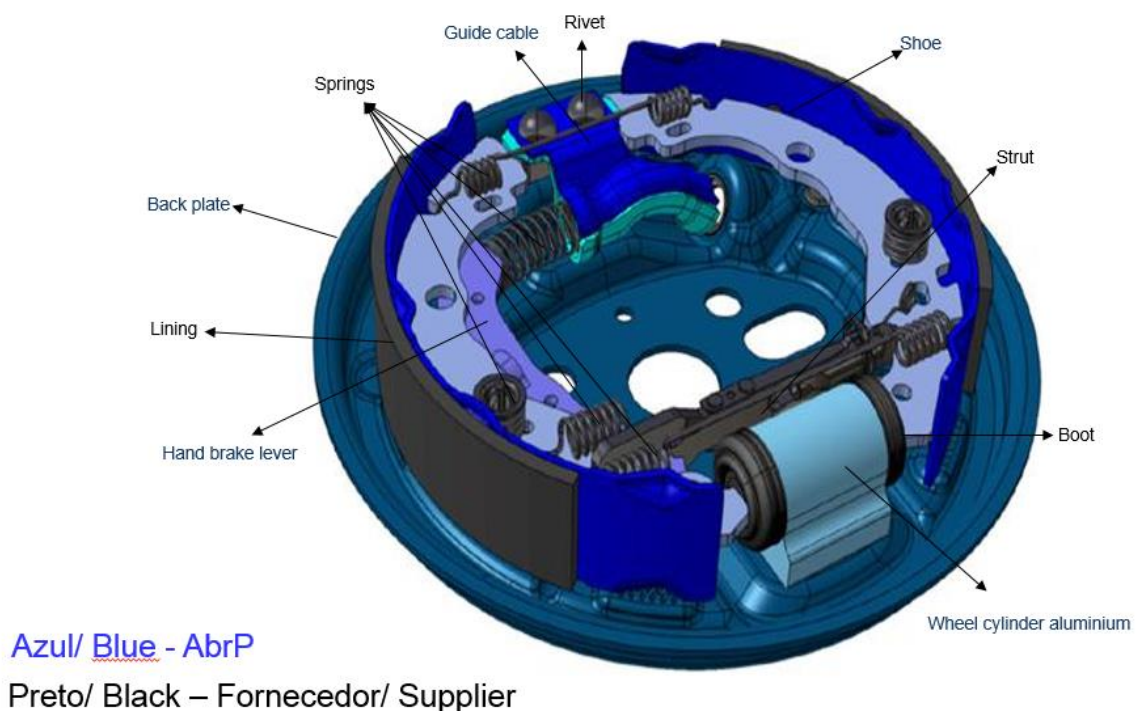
Travão de tambor e seus componentes, adaptado de (CBI, 2017)
